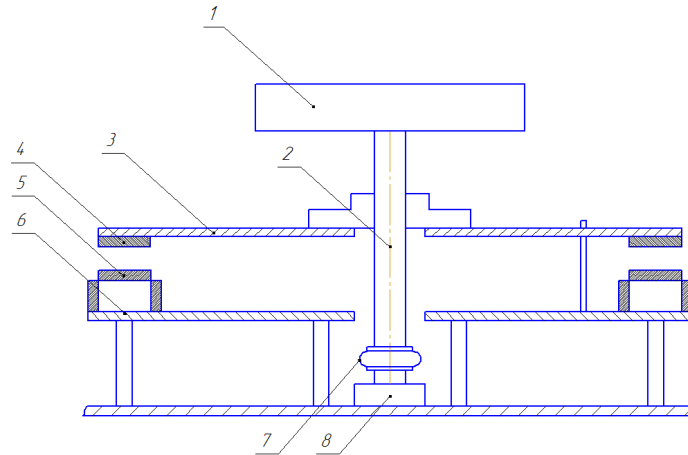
Схема магнітного опорного механізму ударно-відцентрової дробарки
